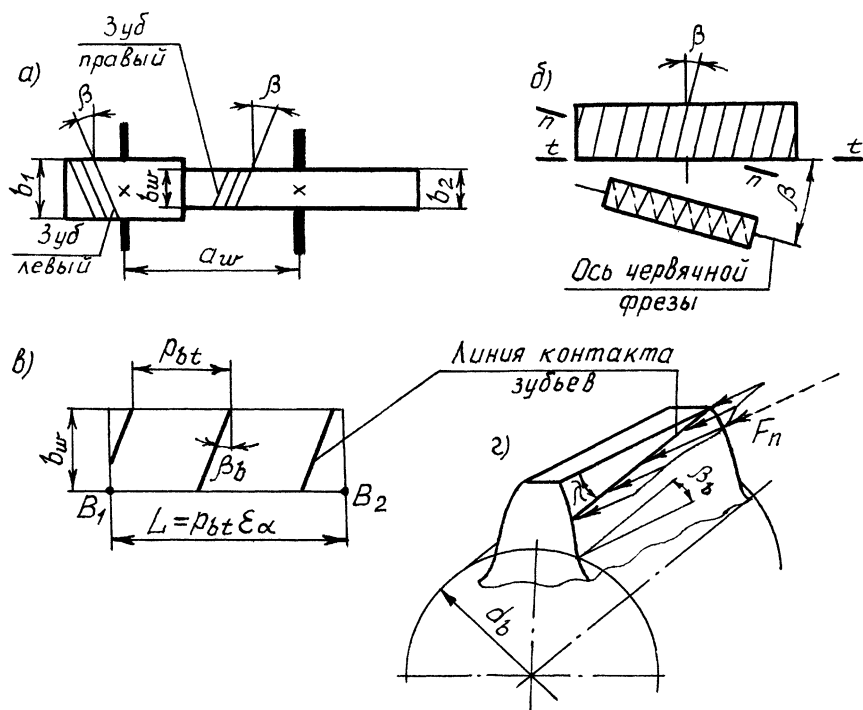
Цилиндрическая косозубая зубчатая передача:
